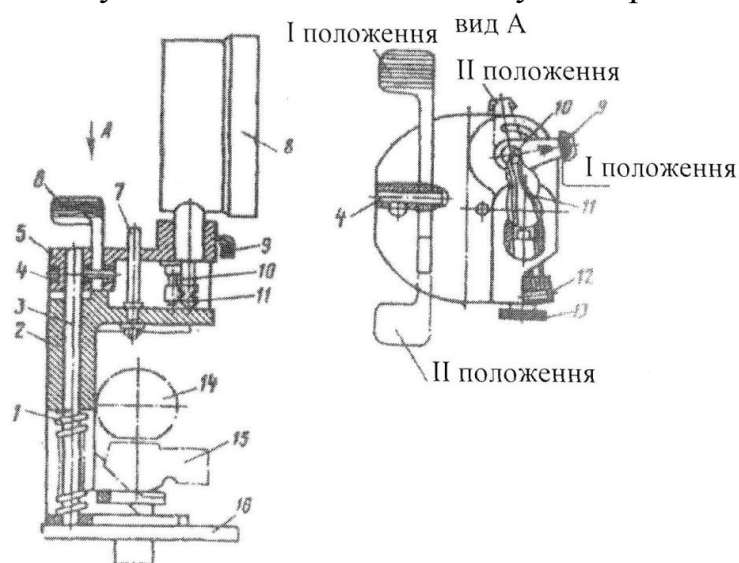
Загальний вигляд приладу КИ-29918: 1 - пружина; 2 - каретка; 3 - напрямна; 4 - вісь; 5 - корпус; 6 - кулачок; 7 - стержень; 8 - індикатор; 9 - важіль; 10 - кулачок гальма; 11 - пластинчасті пружини; 12 - гвинт; 13 - стопорний гвинт; 14 - валик декомпресора двигуна; 15 - коромисло двигуна; 16 - тарілка пружини клапана двигуна.
